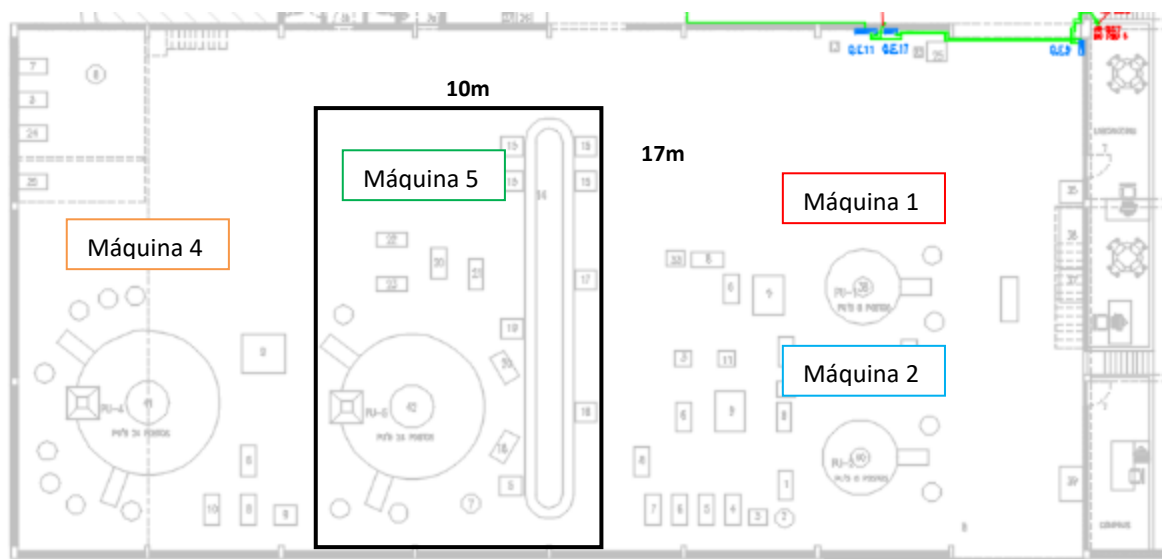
Planta original das máquinas 1, 2, 4 e 5
